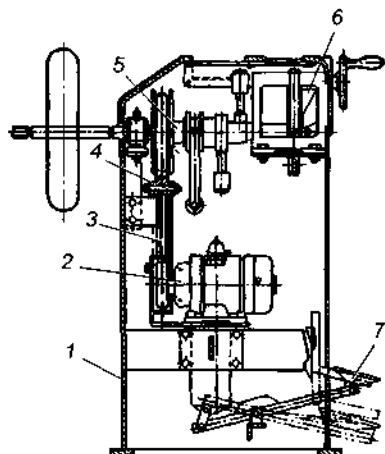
Балансировочный станок для колес легковых автомобилей: 1 — корпус; 2 — электродвигатель; 3 — ременная передача; 4 — тормозное устройство; 5 — балансировочный механизм; 6 — резонансный индикатор; 7 — педаль
